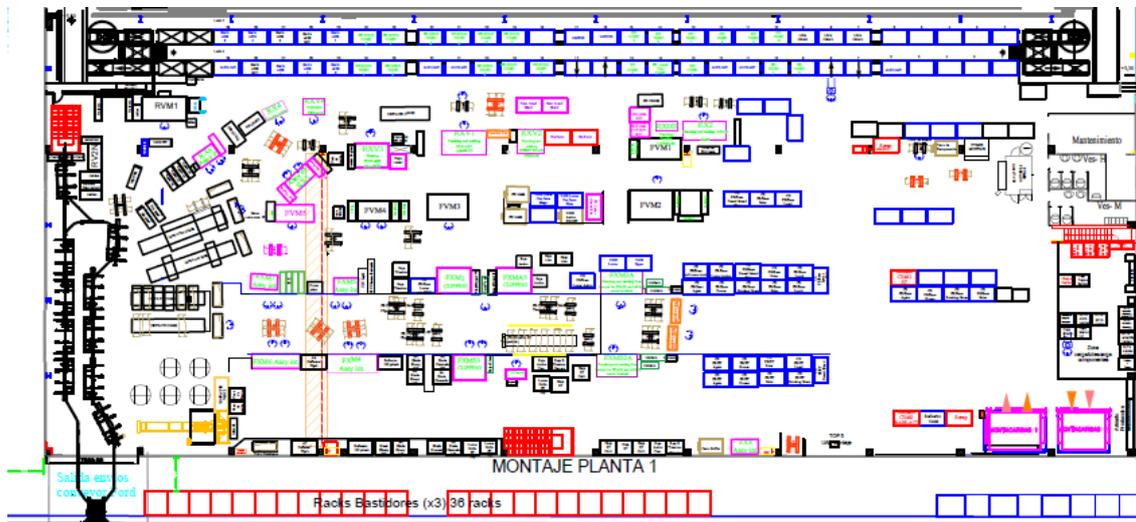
Lay Out Área Montaje (Fuente: Plastic Omnium)
